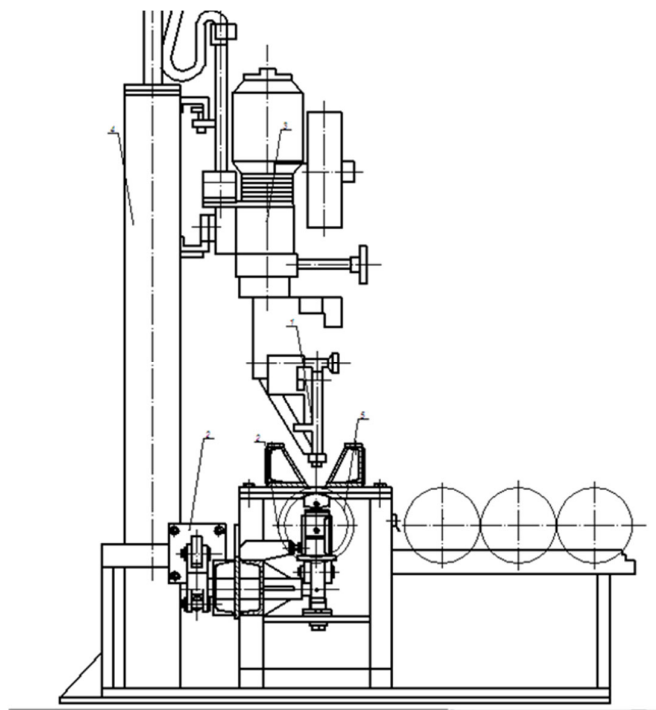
Загальний вигляд спеціалізованої зварювальної установки Р-879 та затискного пристрою
